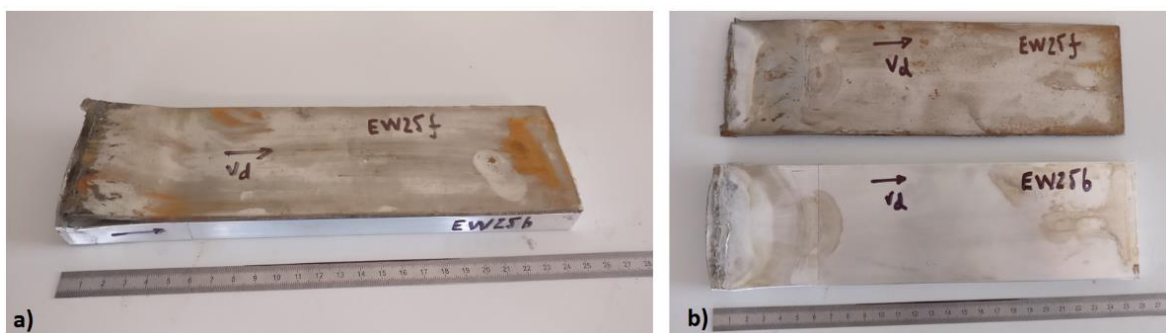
Análise macroscópica da soldadura EW25: a) Peças sobrepostas; b) Peças separadas.
